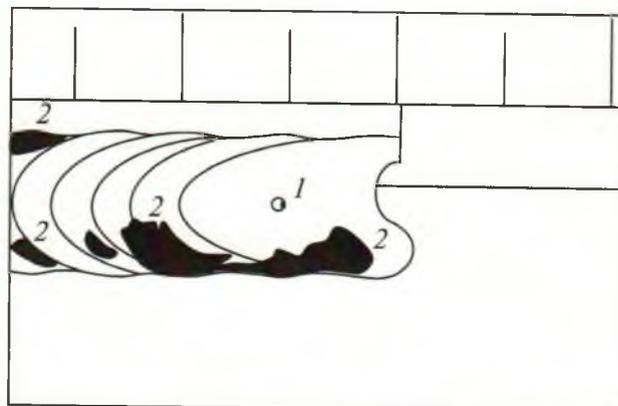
Пора 1 в кратере нахлесточного сварного соединения. Наблюдается также окисление поверхностное в виде пленки оксидов 2 на поверхности шва
